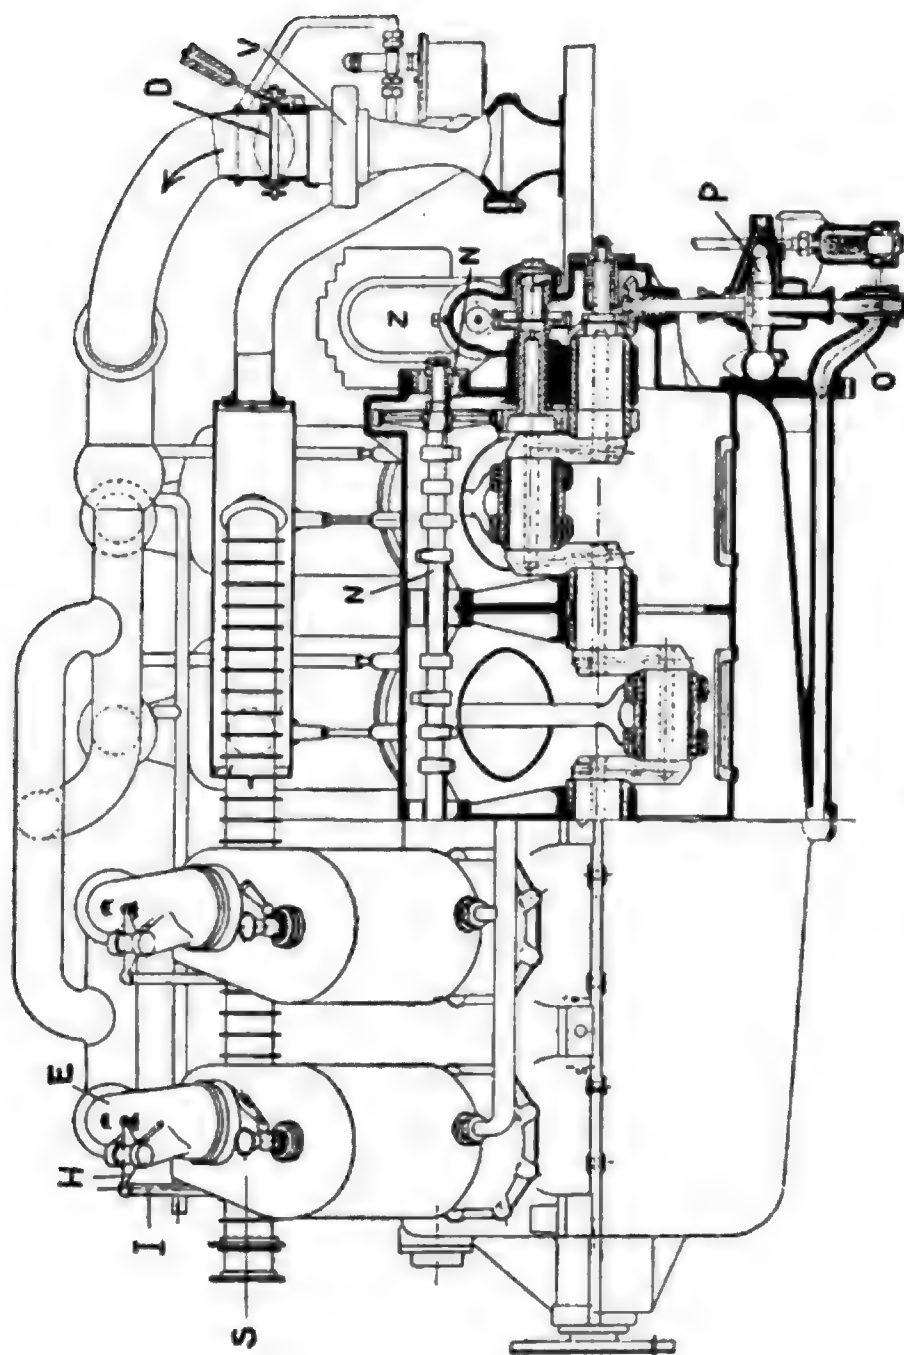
Seitenansicht bzw. Längsschnitt des Körting-Luftschiffmotors.
